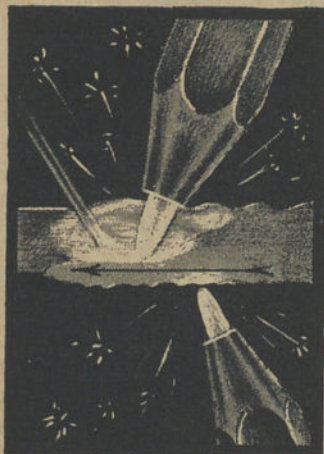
Ataque do lado oposto da soldadura; por outro maçarico.
